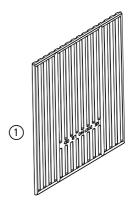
Revêtement de la chambre de combustion FINA DS
